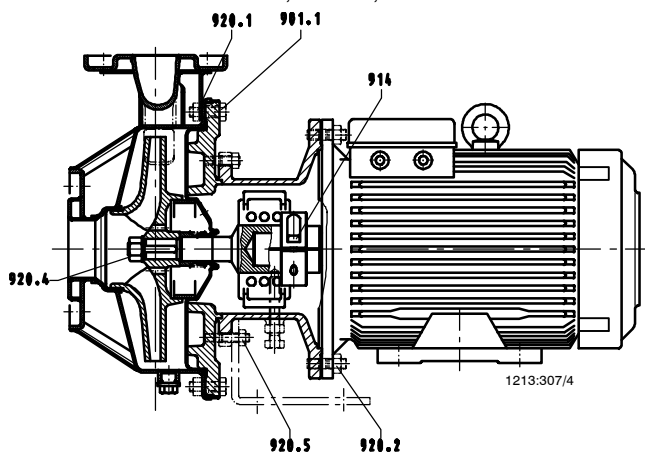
Места затяжки резьбовых соединений Etachrom BC с диаметром рабочего колеса 250, 50-200, 65-200, 80-200
